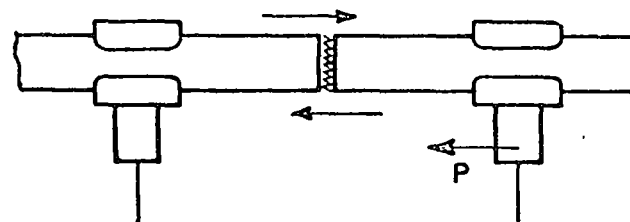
Principio del soldeo a tope por chisporroteo.
